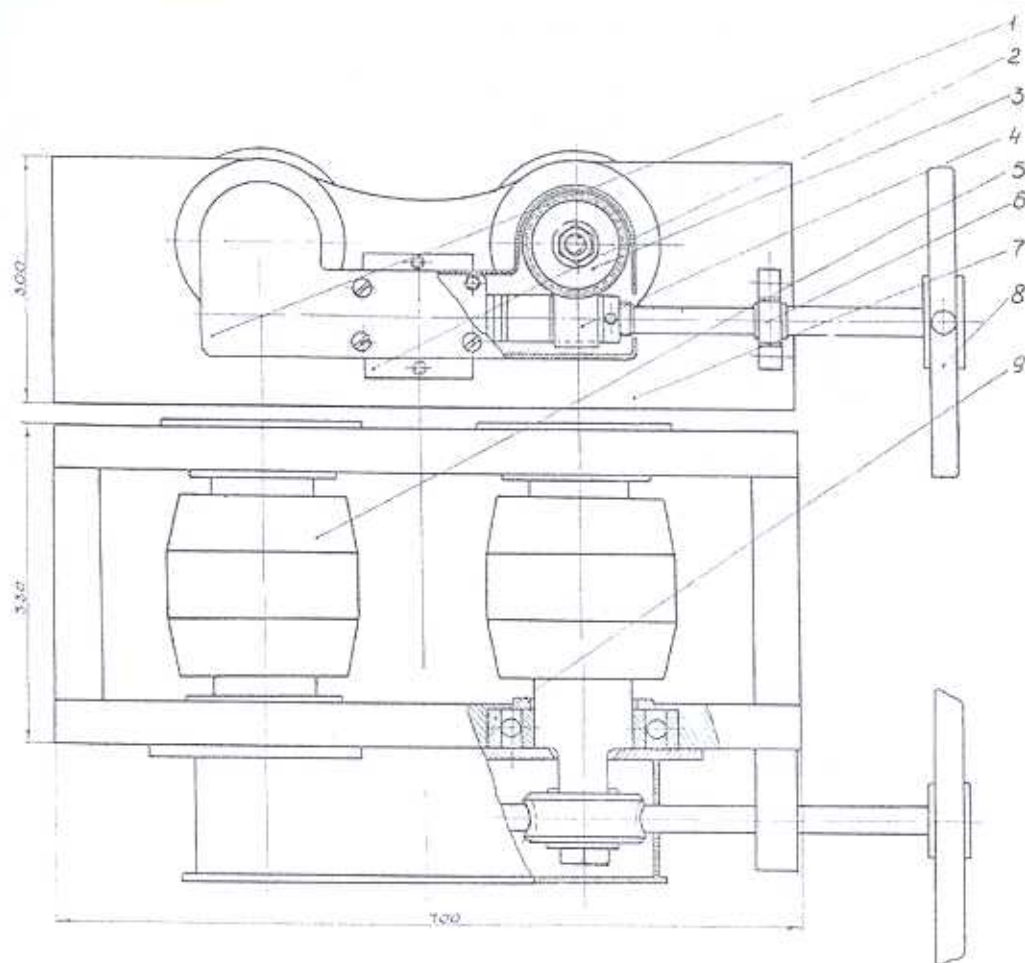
Роликовая опора для установки и проворачивания ротора:
